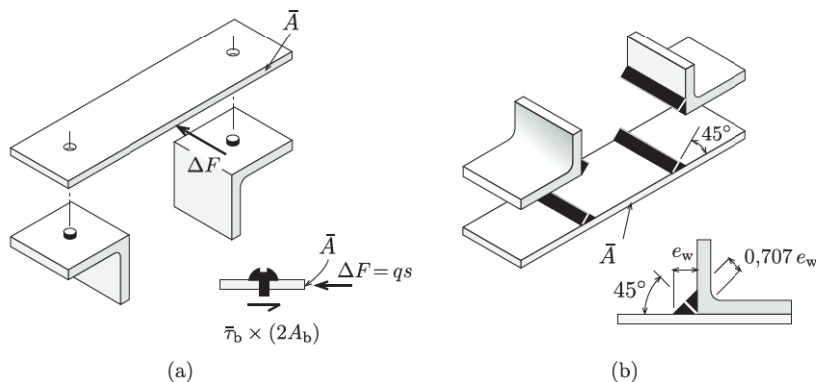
Ligações: (a) parafusada; (b) soldada.
